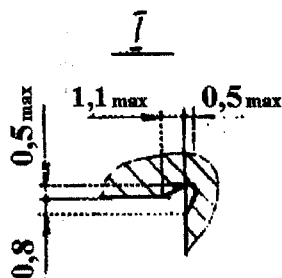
Чертеж внутреннего кольца роликоподшипника 92705
